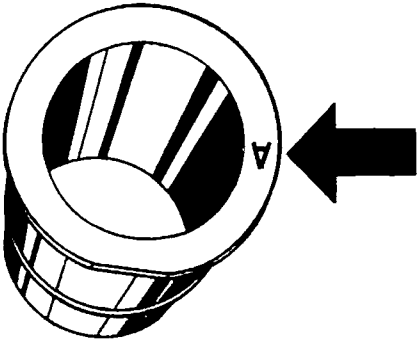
/1 Kennzeichnung der Zylinderlaufbühnen-Toleranzklasse
